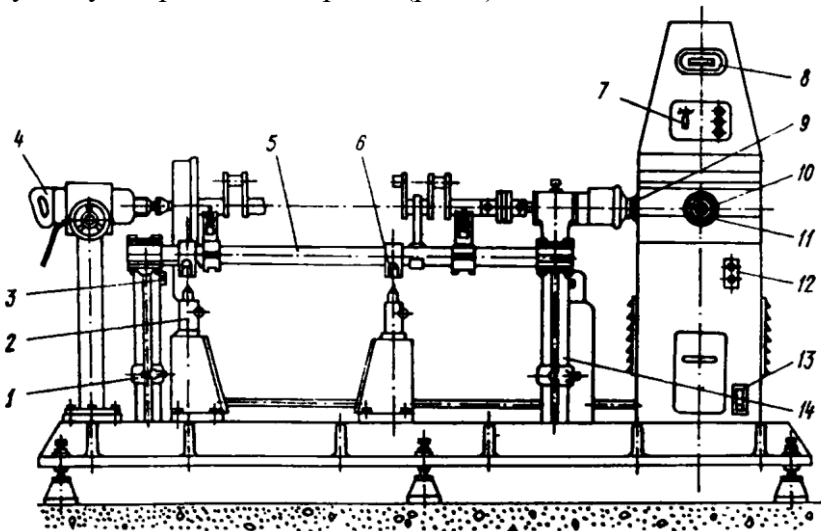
Верстат для динамічного балансування колінчастих валів:
